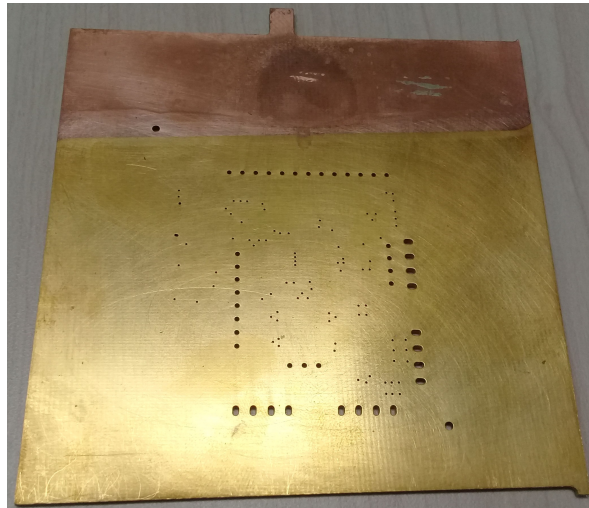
Resultado final de electrodeposición sobre la placa FR4.
